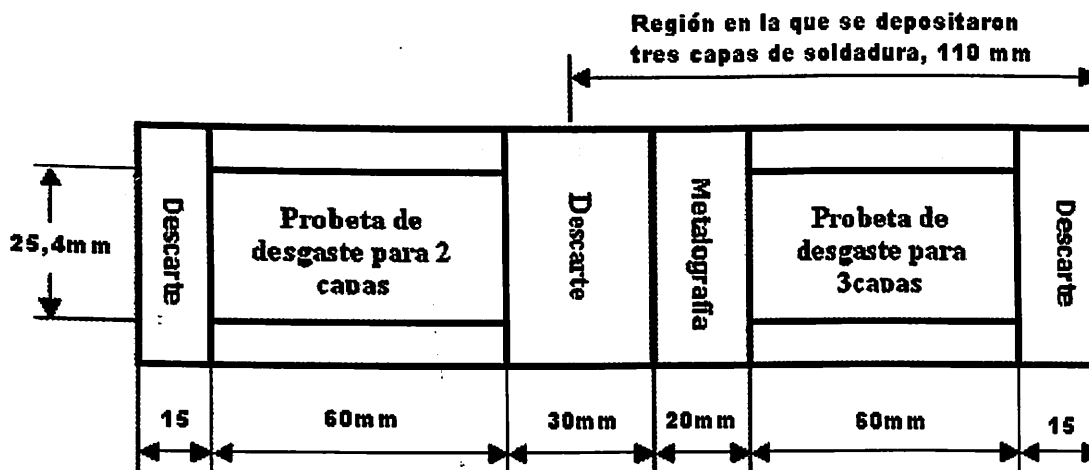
Esquema del cupón y dimensiones de corte de las probetas.
